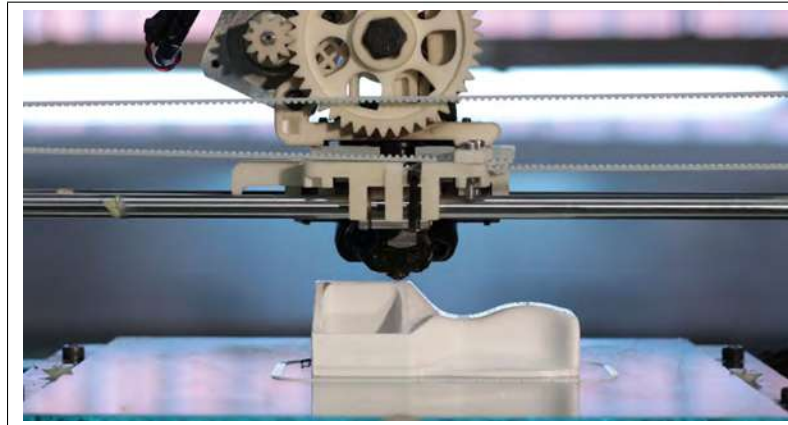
Técnica de impresión de prototipos 3D mediante la deposición aditiva de material.
